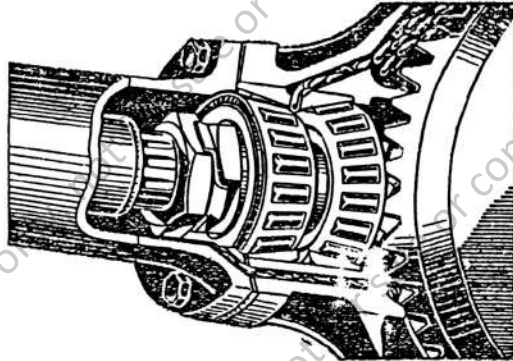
Схема смазки подшипников ведущей шестерни главной передачи
